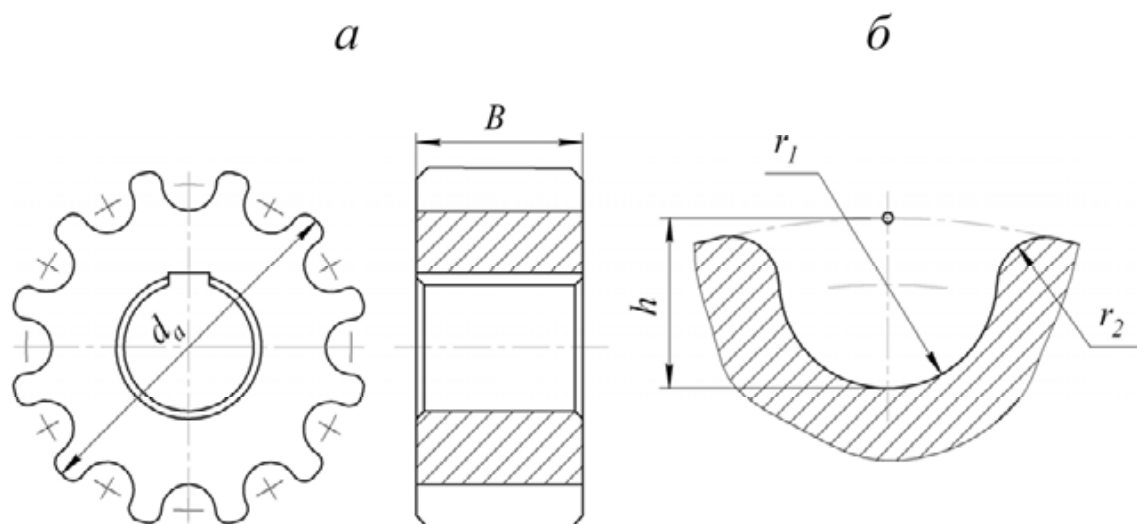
Шкив зубчато-ременной передачи с зубьями полукруглого профиля (а) и его сечение (б)
